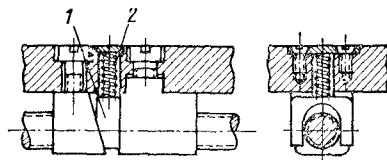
Втулка подшипника с наружной конической поверхностью: 1 — втулка; 2 — гайка.
